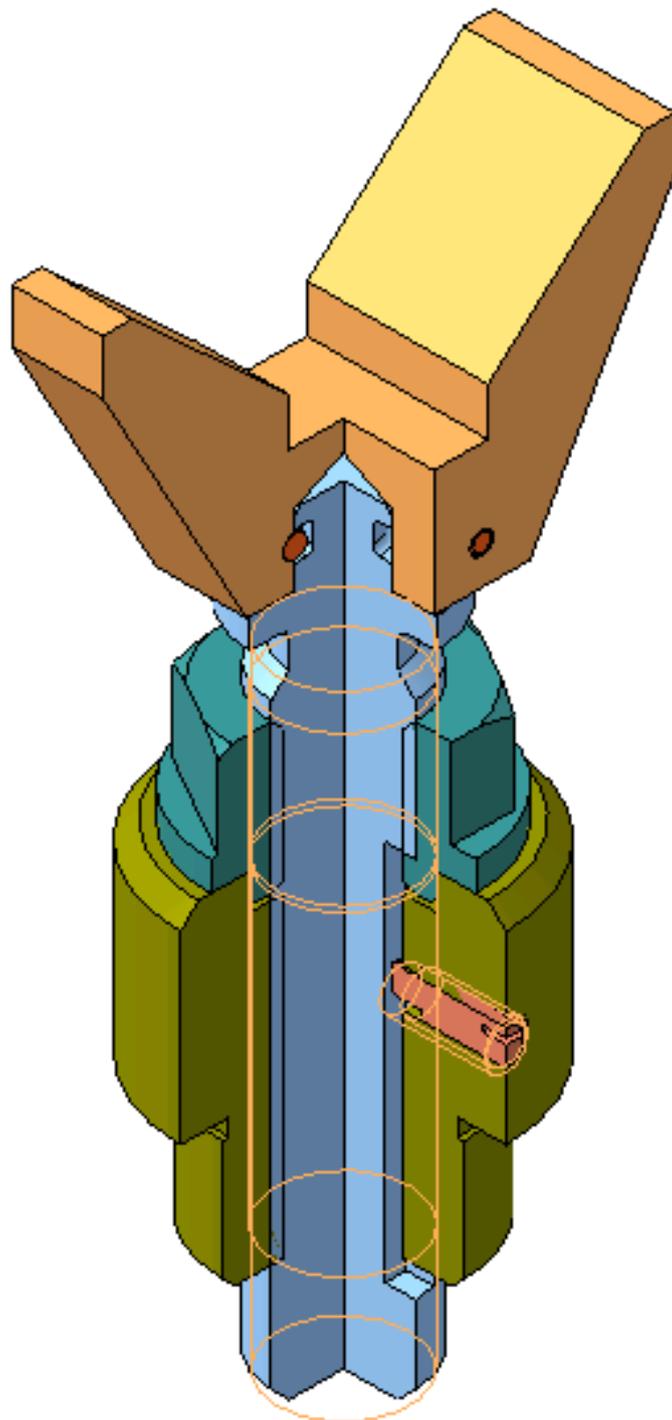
3D-модель сборки изделия «Подпорка винтовая встроенная»
